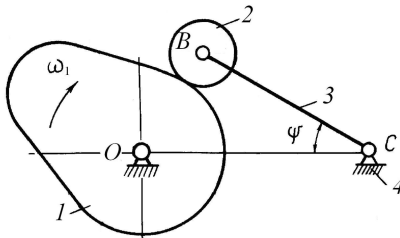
Схема кулачкового механизма с вращательным движением толкателя с роликом
